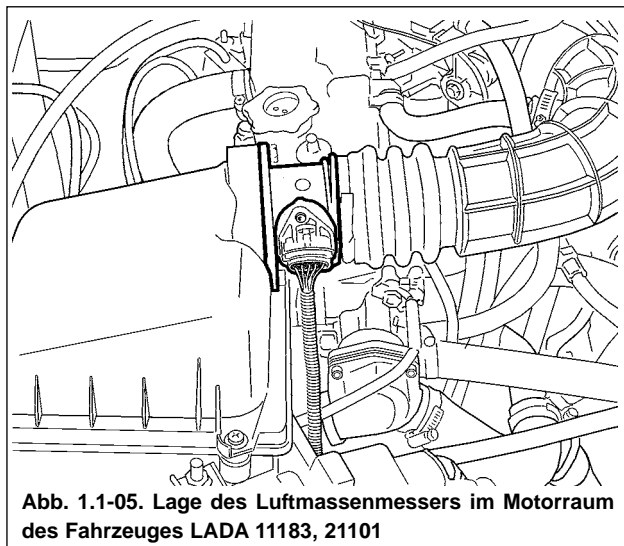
Lage des Luftmassenmessers im Motorraum des Fahrzeuges LADA 11183, 21101
